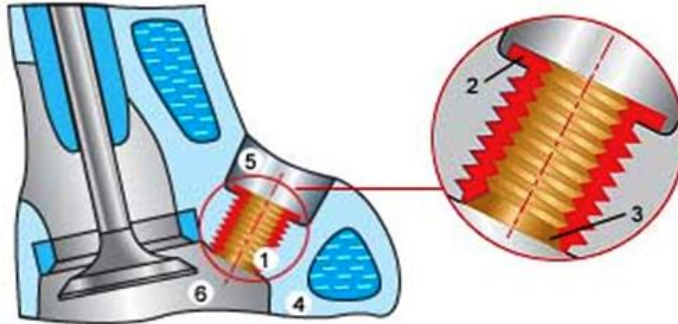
Резьбовая вставка с опорным фланцем в головке блока:
